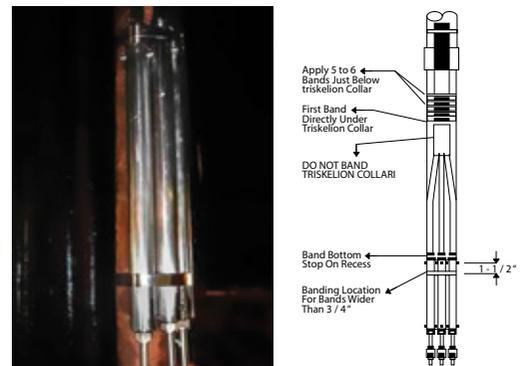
Conexión Eléctrica QCI de fondo del pozo.
